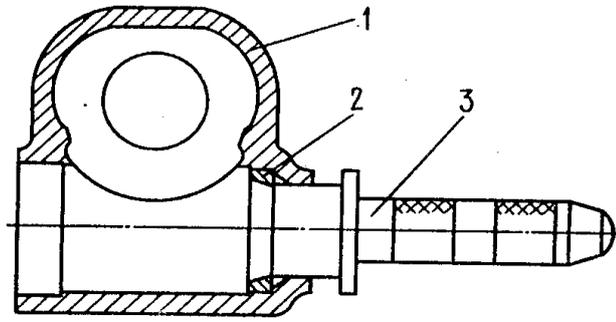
Remoción del anillo exterior del cojinete superior del sinfín con ayuda del extractor 67.7853.9541:
